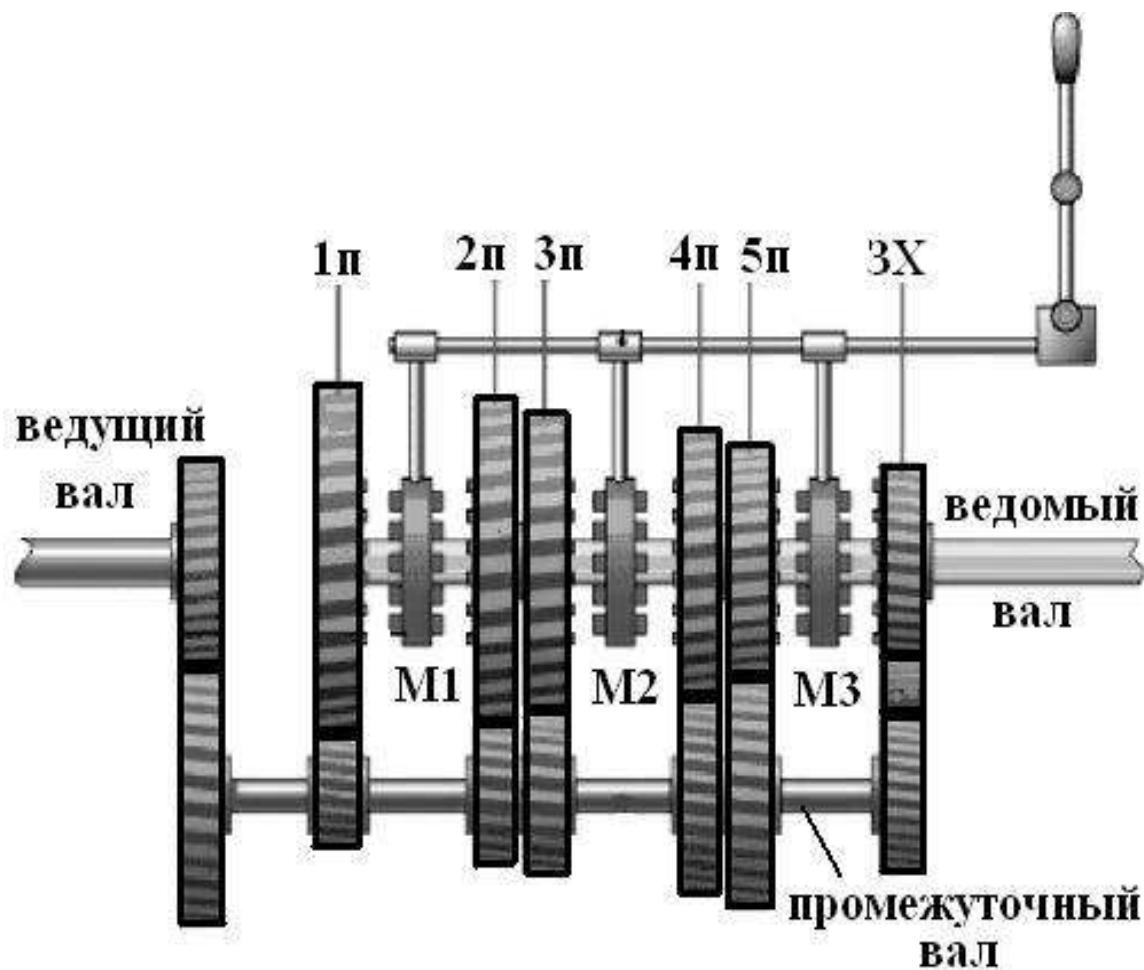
Схема трехвальной коробки передач[23]
